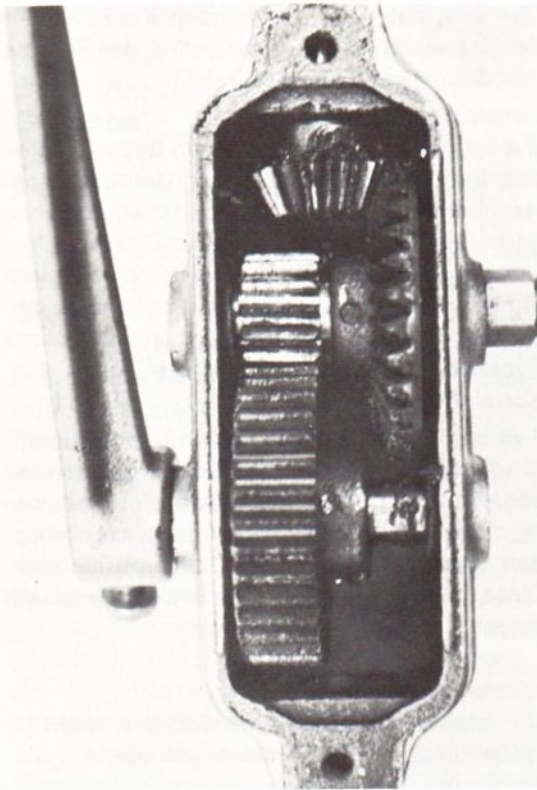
Das Gehäuse der Handbohrmaschine ist geöffnet.
